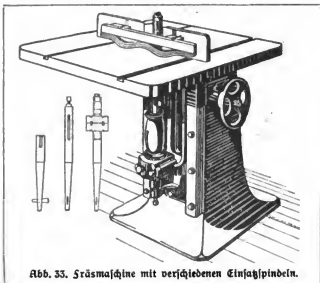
Fräsmaschine mit verschiedenen Einspindeln.
